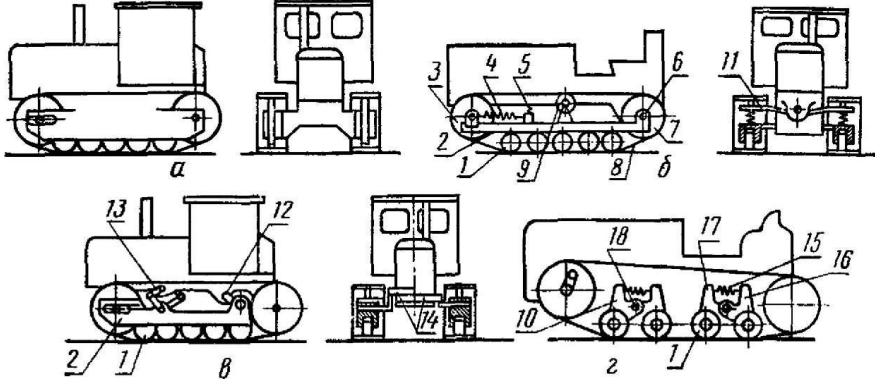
Схеми підвісок гусеничних тракторів: а - тверда; б - напівтверда триточкова; в - напівтверда чотириточкова; г - пружна балансирна; 1- опорний коток; 2 - гусеничний візок; 3 - напрямне колесо; 4 - натягувальний пристрій; 5 - гумова подушка; 6 - задній шарнір; 7 - ведуча зірочка; 8 - гусениця; 9 - підтримувальний ролик; 10 - каретка; 11 - ресора; 12,13,16,17 - напрямні важелі; 14 - торсіони; 15 - пружина; 18 – вісь.
